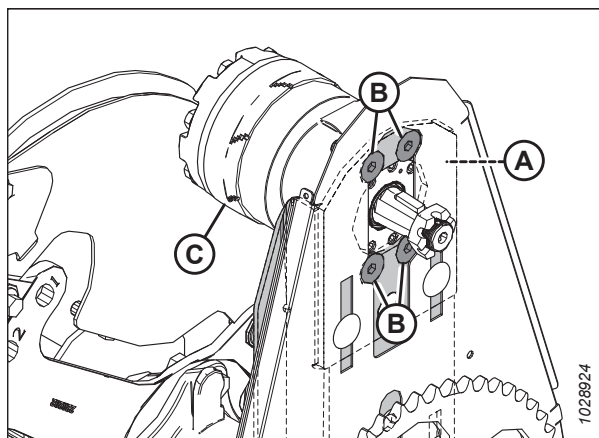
Tornillos de montaje del motor del mando del molinete
